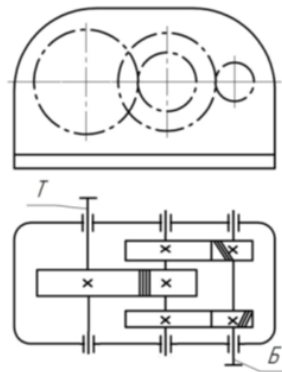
Двухступенчатый горизонтальный редуктор с раздвоенной быстроходной ступенью
